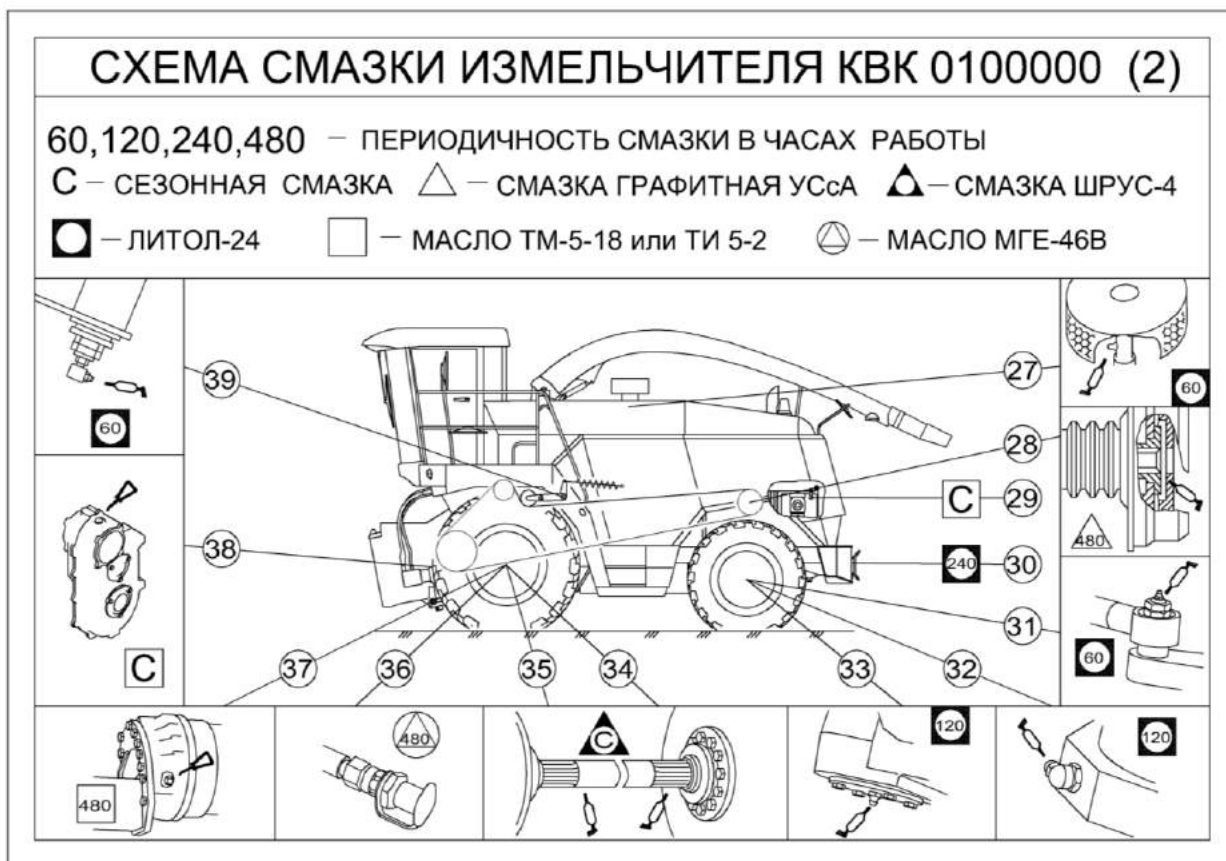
Схема смазки измельчителя КВК 0100000 (вид слева)
